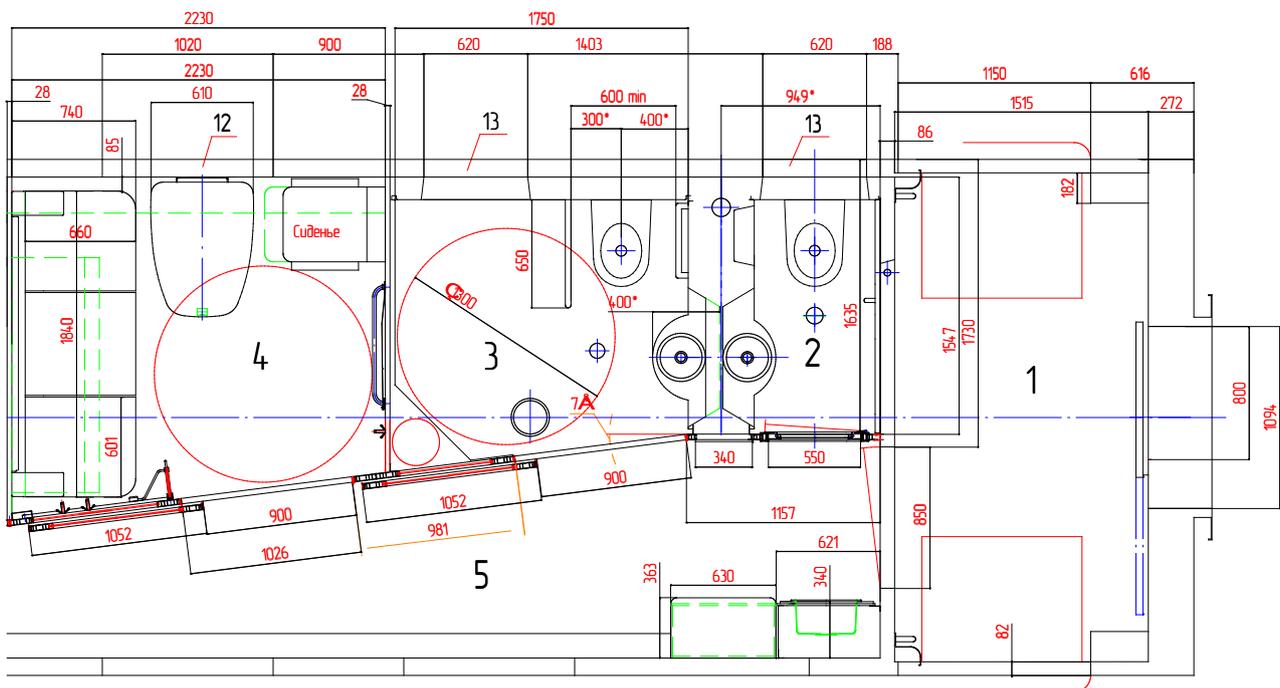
Планировка нетормозного конца вагона модели 61-4445 с помещениями для инвалидов-колясочников: 1 — увеличенный тамбур нетормозного конца вагона; 2 — туалет; 3 — туалет для инвалида; 4 — купе для инвалида и сопровождающего лица; 5 — коридор нетормозного конца вагона
